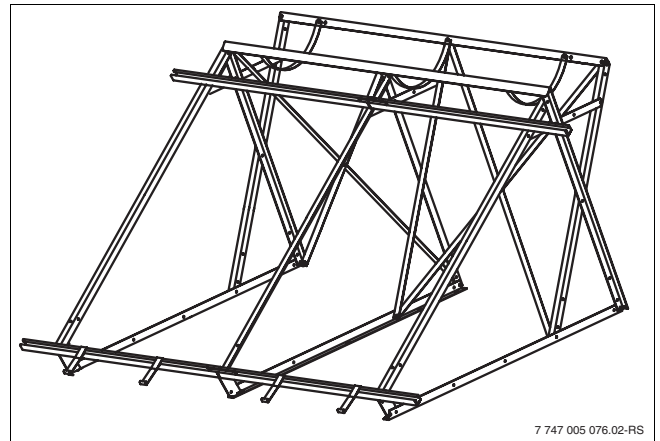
Vista geral do suporte para telhados planos (aqui, sistemas de 300 l)
